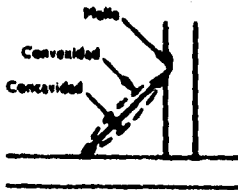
SOLDADURA EN ANGULO
